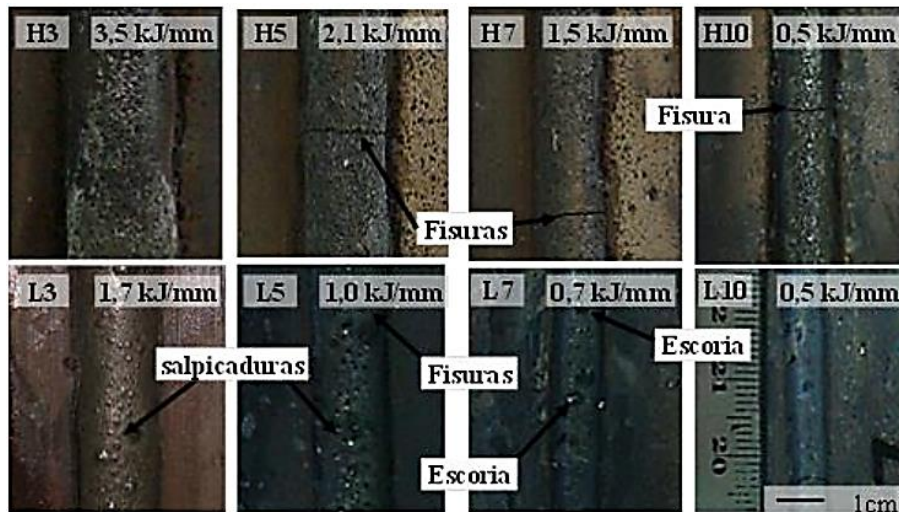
Vista superior de los cordones bead on plate. Soldados sin protección.
